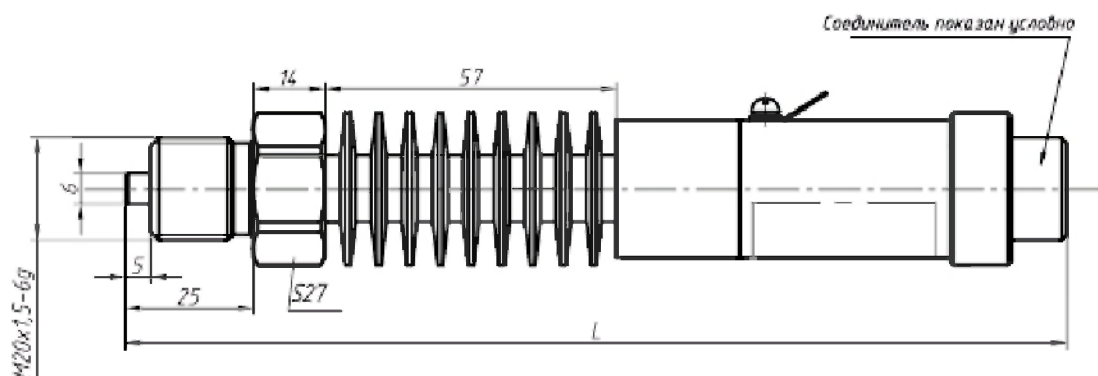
Габаритный чертеж преобразователей разности давлений с кодами конструктивного исполнения К21 и К31 (по таблице А.14)
